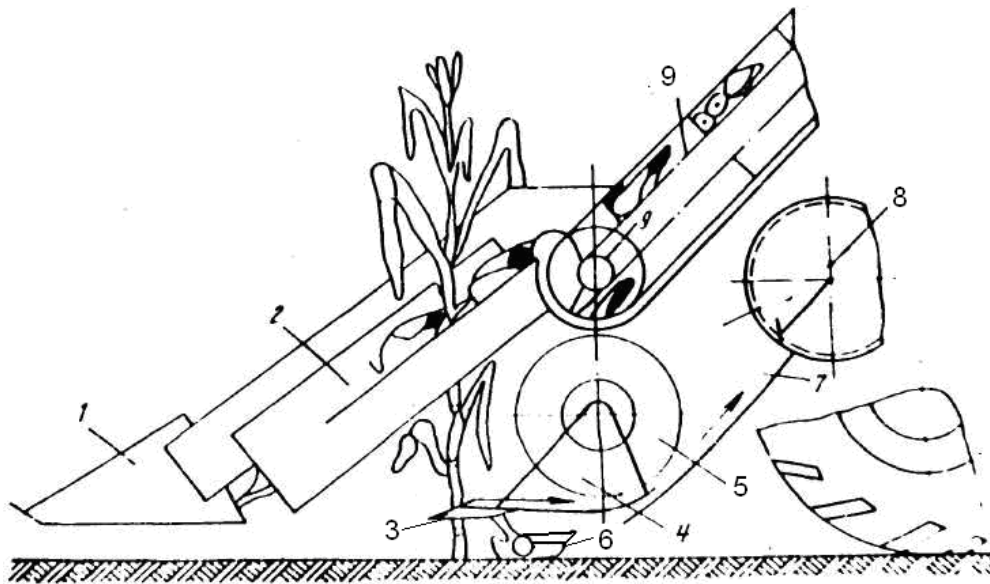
Схема жатної частини з шарнірно-закріпленим днищем шнека
